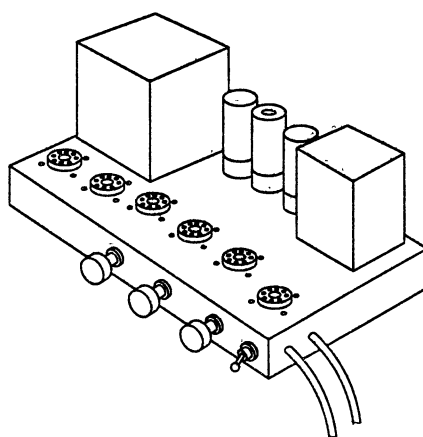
Пример однопанельной конструкции прибора на цельнометаллическом сварном коробчатом шасси
